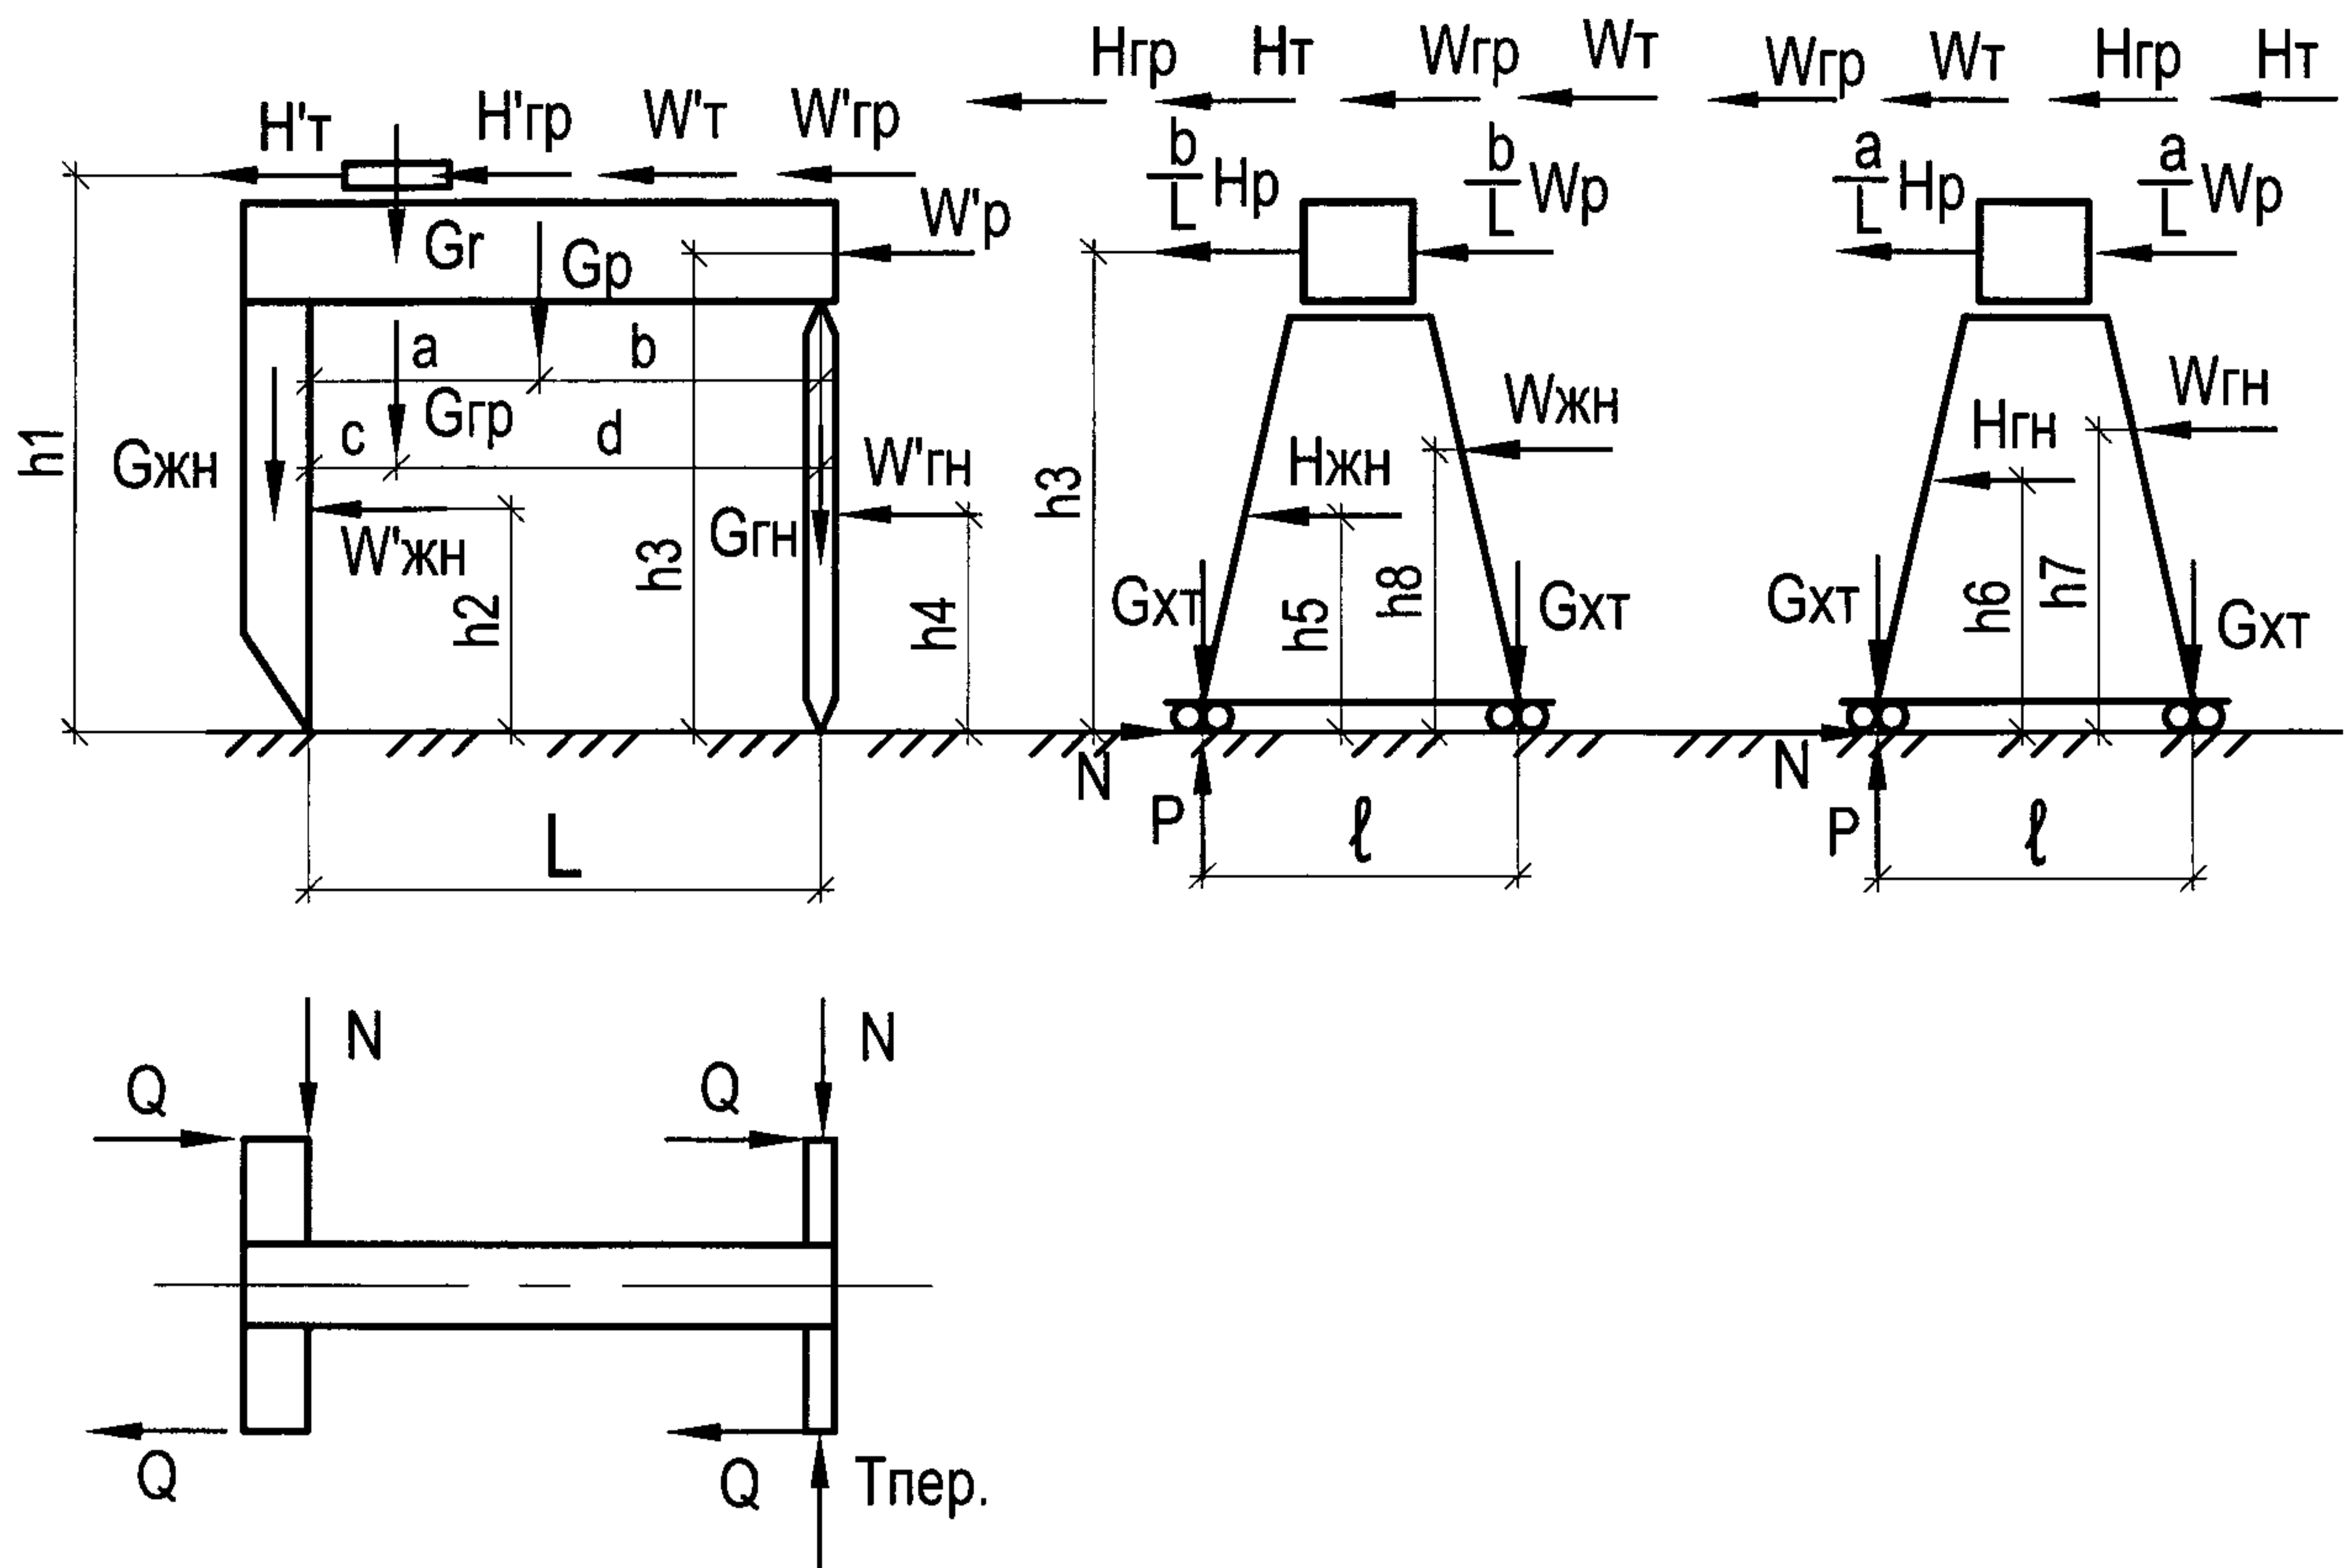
Схема приложения нагрузок к козловому крану
